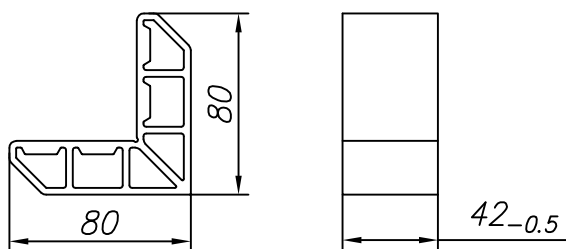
Изготовление соединителя углового FLGU.400.0914
